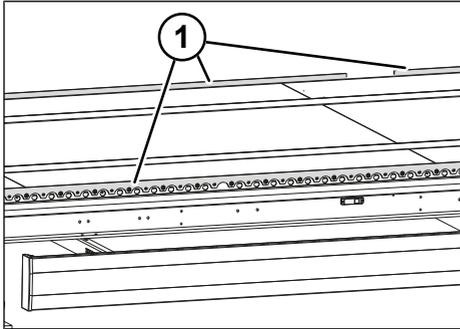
Multi Screw no quadro exterior Multi Lock
